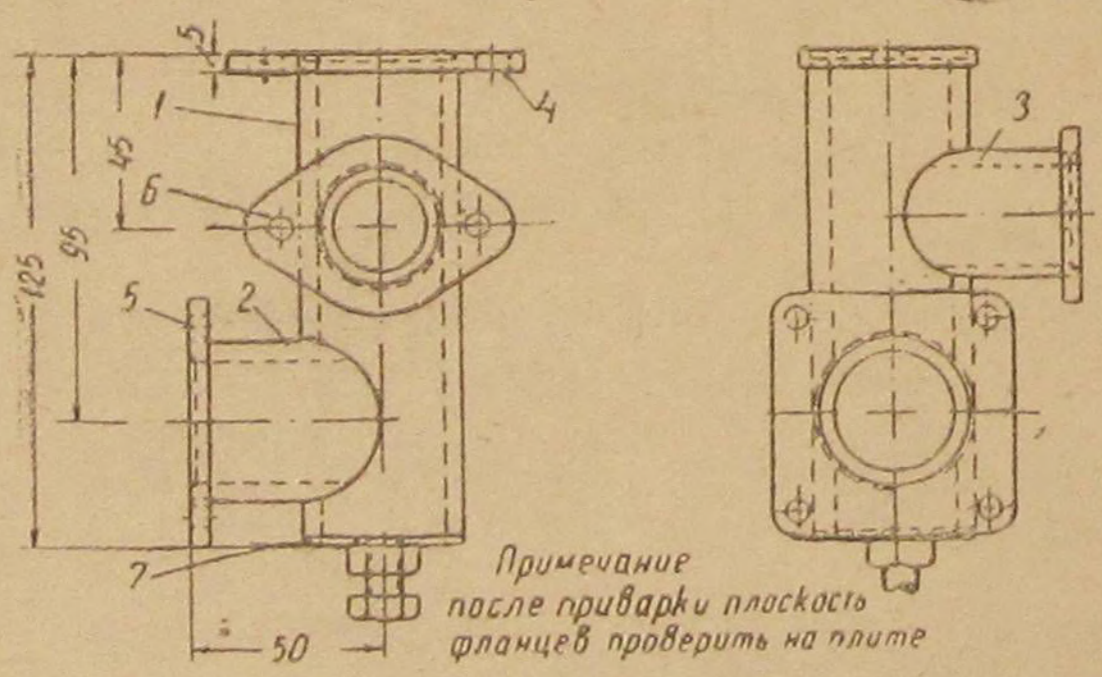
Переходный патрубок для монтажа смесителя газа и карбюратора:
